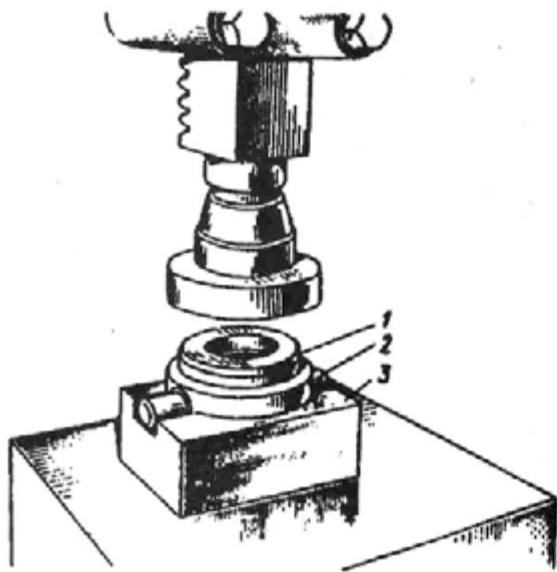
Запрессовка подшипника в обойму на прессе:
